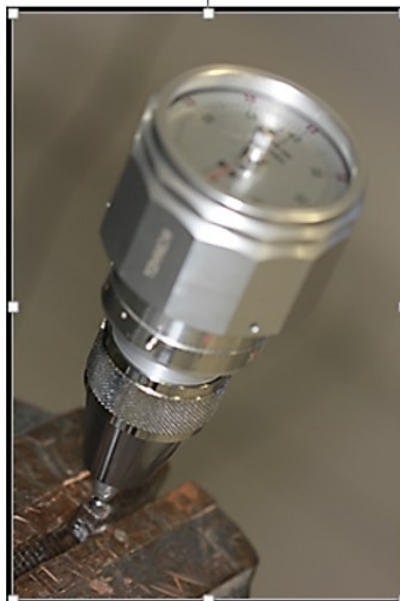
Conjunto corpo de prova/torquímetro fixados na morsa prontos para receberem o torque inicial.
